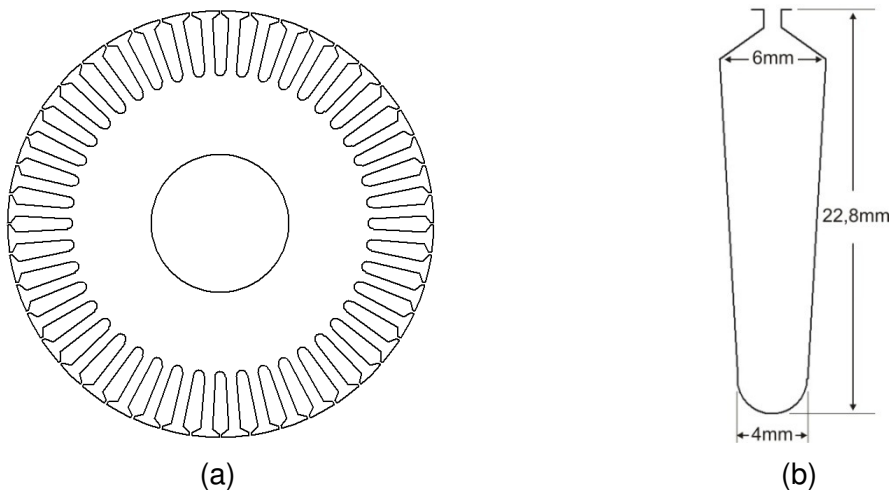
(a) Vista geral do rotor do primeiro rotor. (b) Detalhes da ranhura do rotor do motor 1.
